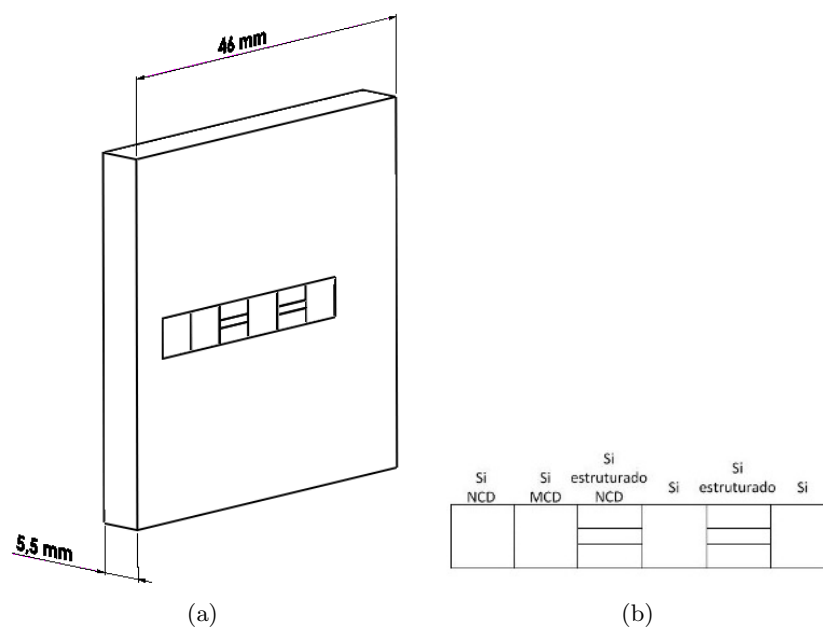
(a) Desenho da placa com os inserts; (b) Disposição dos inserts na ferramenta do molde.
